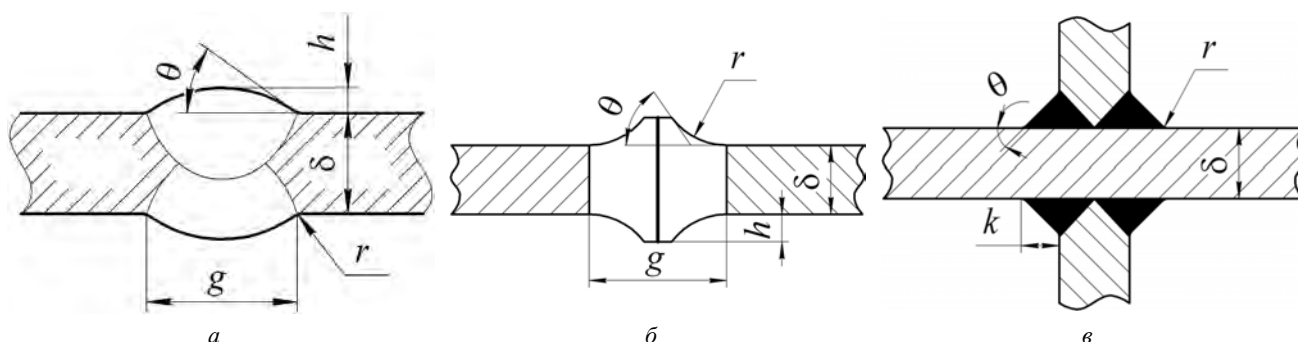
Сварные соединения с двусторонним симметричным усилением а – стыковое соединение, выполненное сваркой плавлением, б – стыковое соединение, выполненное КСС оплавлением, в – крестообразное соединение
